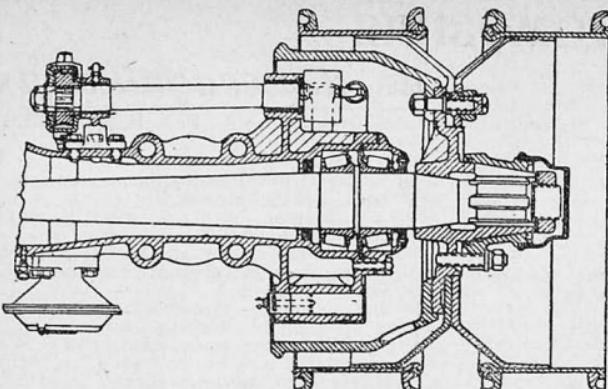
Установка подшипника колеса непосредственно на полуосях
